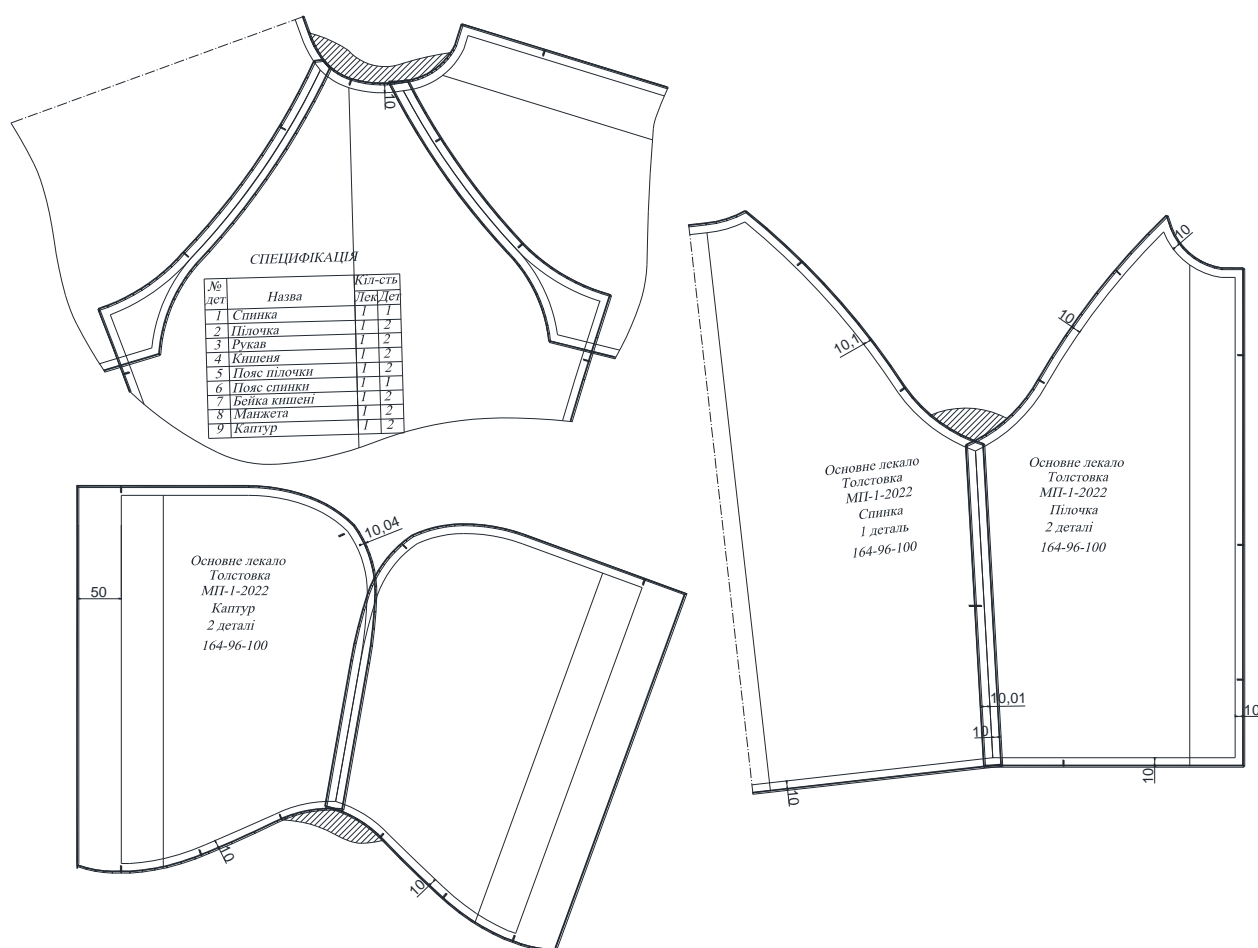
Схема перевірки спряження деталей толстовки
